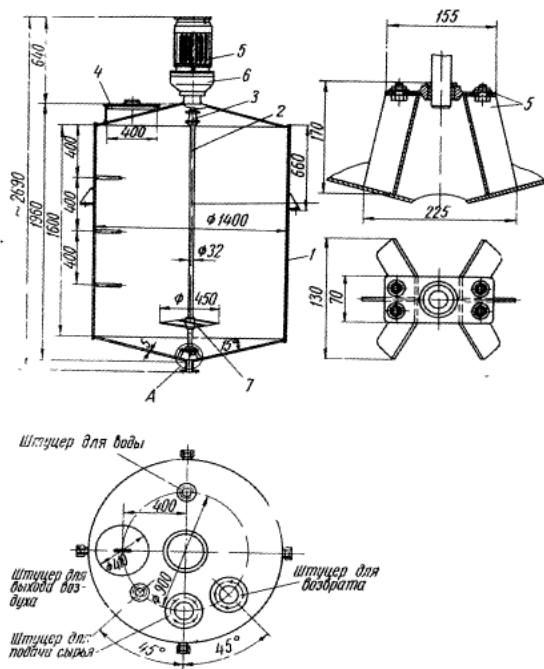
а. Смеситель для приготовления питательной среды (общий вид)
